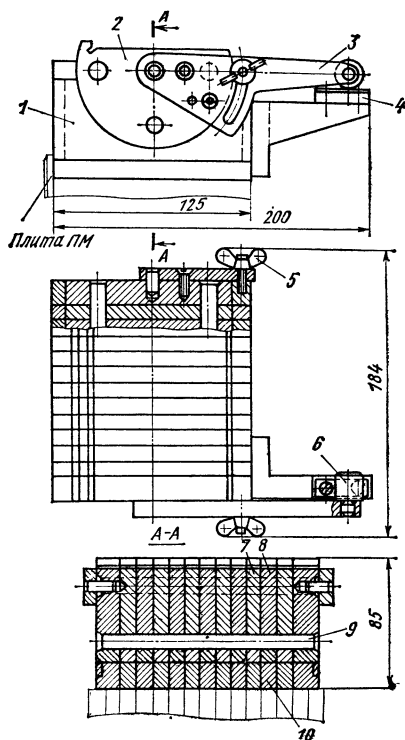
Пример доработки заготовки магнитного переходника, используемого при обработке детали со скосом
